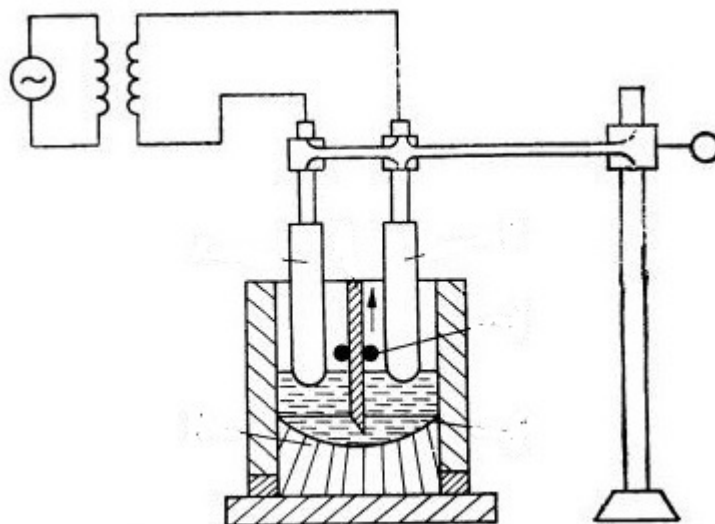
Схема ЕШП двохшарового виливка [1]
